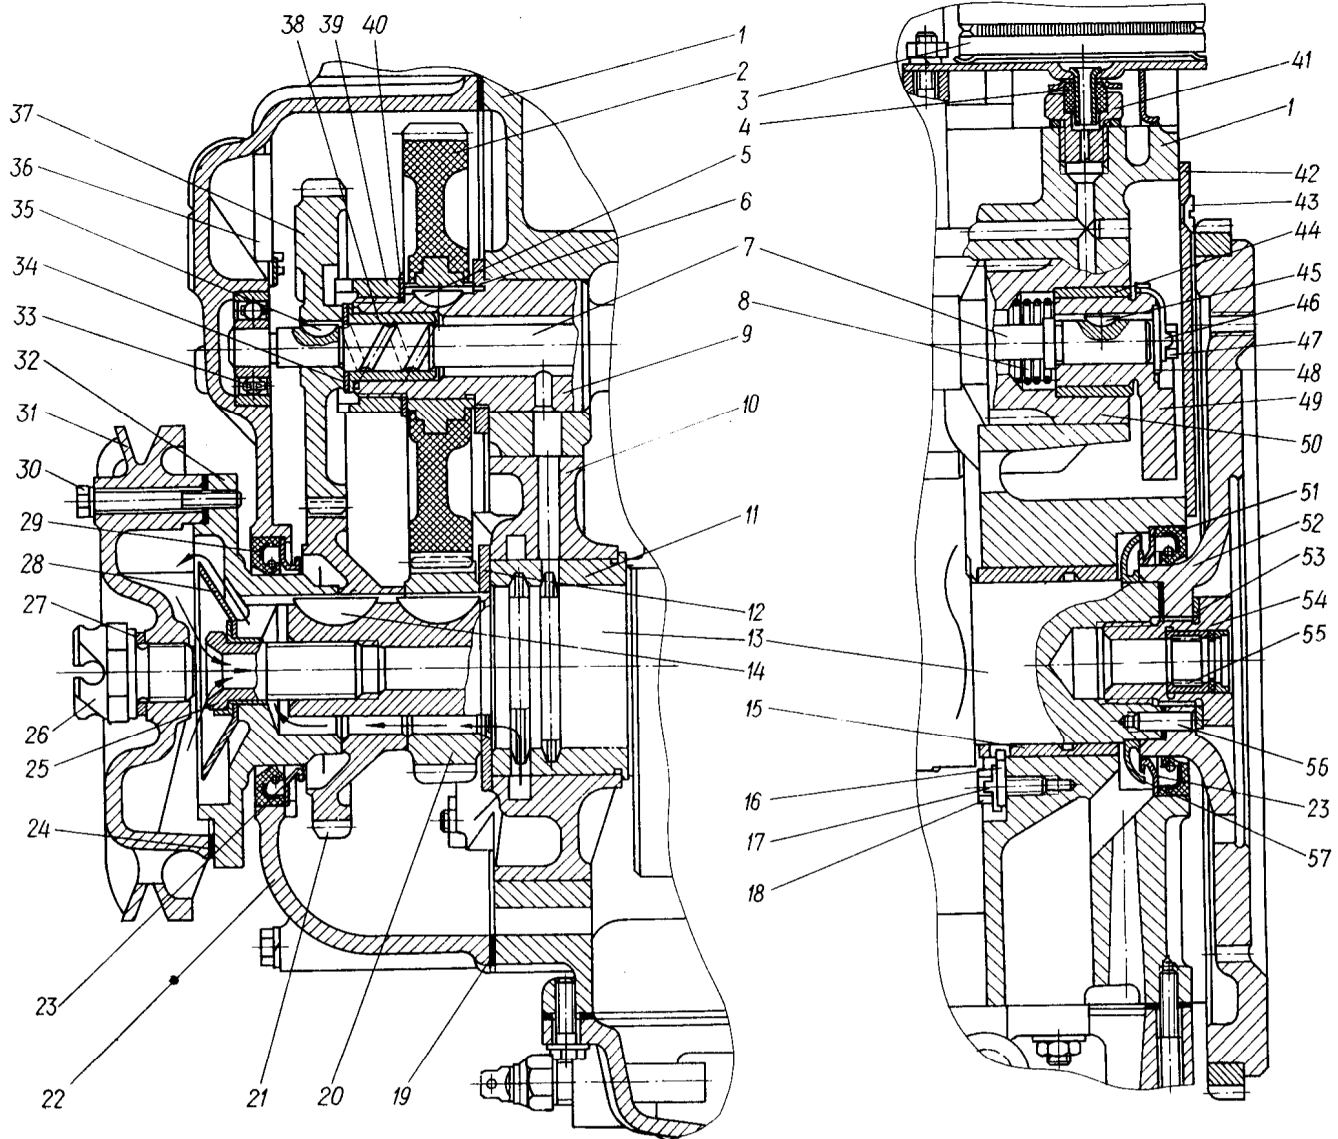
Привод распределительного вала, балансирующего механизма и задний коренной подшипник:
